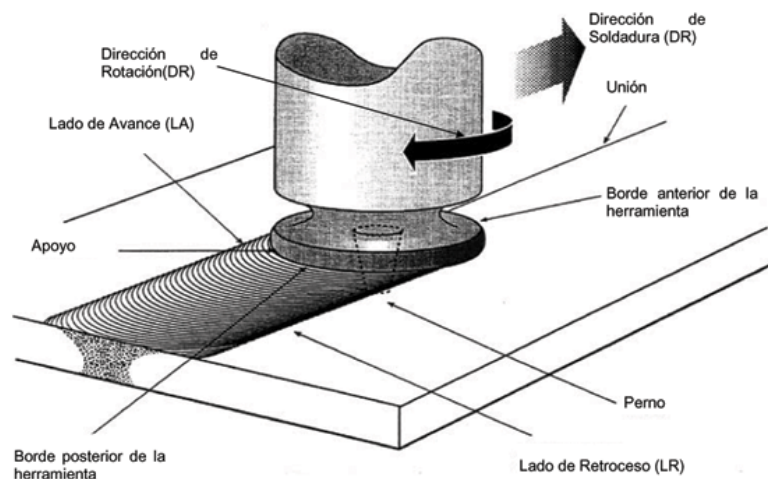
Esquema del proceso de Soldadura por Fricción-Agitación.
